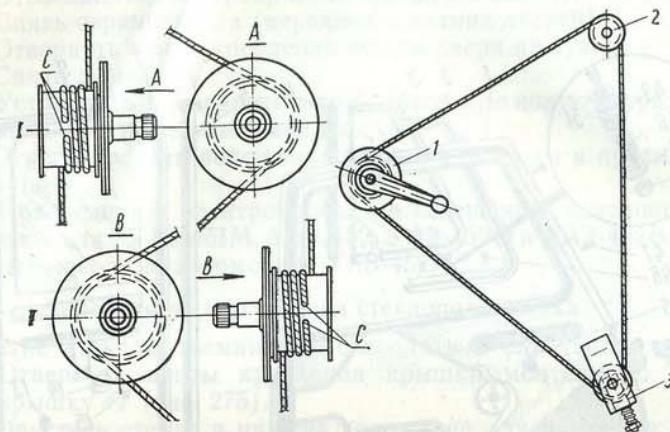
Схема намотки троса на барабан и установка стеклоподъемника:
